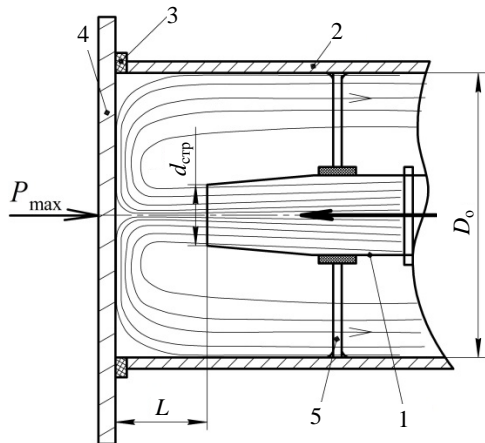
Схема струйного устройства для реализации процесса реверсивно-струйной очистки
